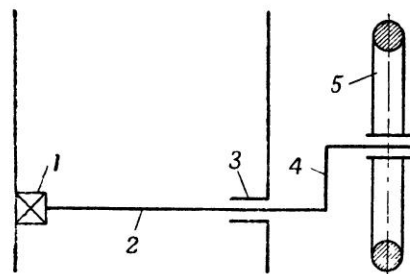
Схема стержневой подвески с поперечным расположением стержней.
